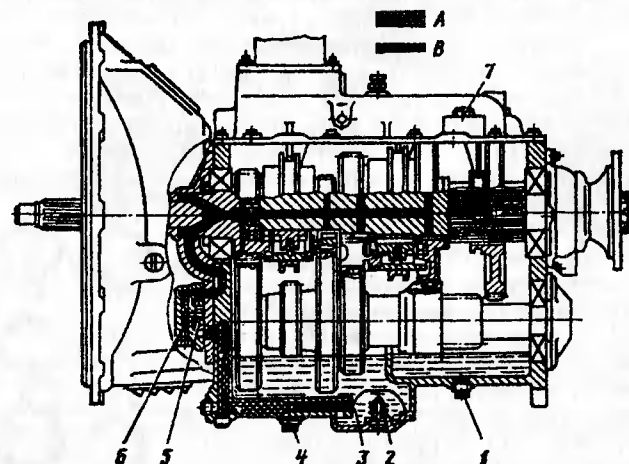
Схема системы смазки коробки передач:
